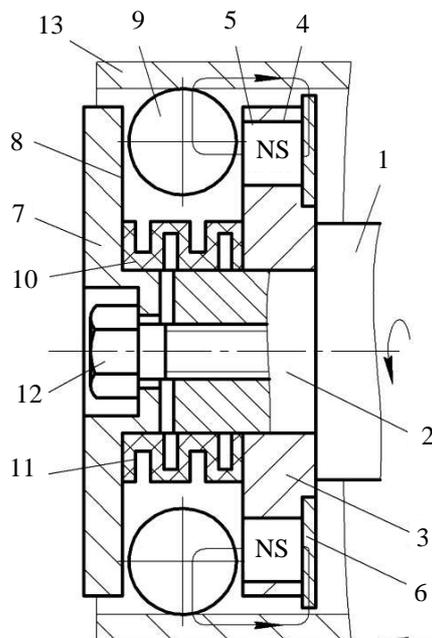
Конструкция инструмента для СМДН с регулируемой по ширине кольцевой камерой
